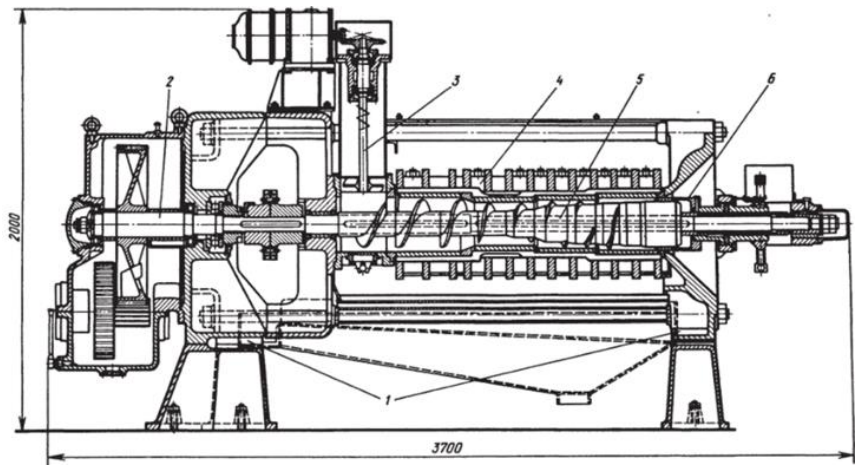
Схема форпреса: ФП 1 – станина; 2 - привід преса; 3 – вертикальний вал; 4 – зерний барабан; 5 - шнековий вал; 6 – регулятор тиску конусного типу
